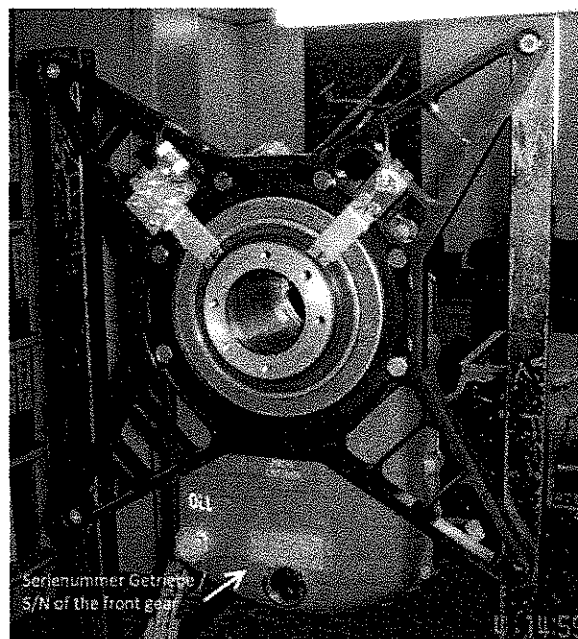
/ figure 1: Anbringung der Getriebeseriennummer / place for the gear s/n
